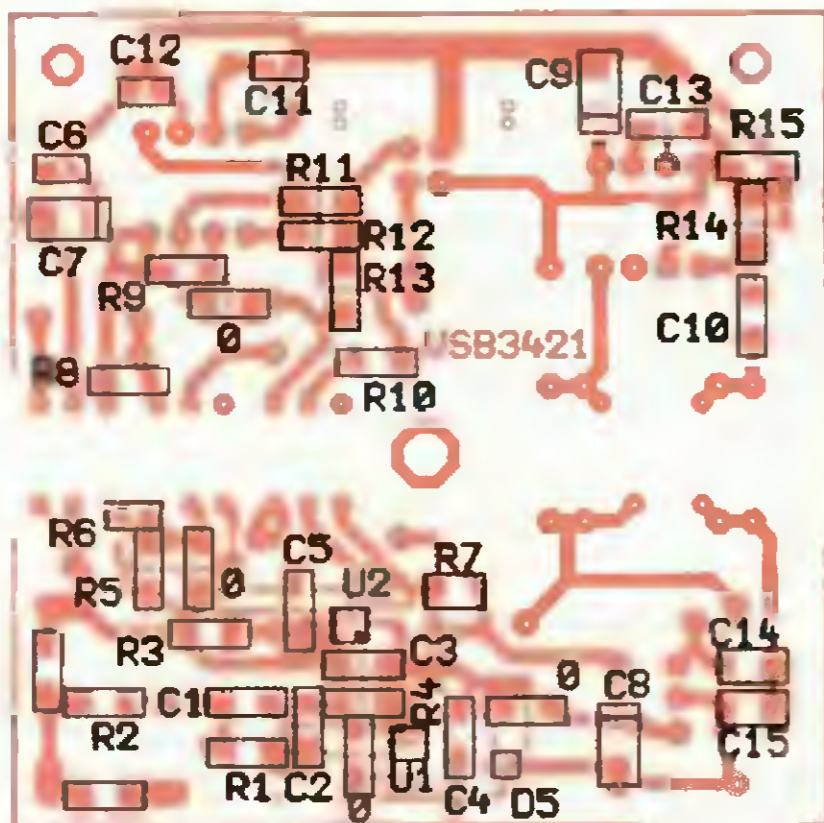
Deska s plošnými spoji (62 x 61 mm)
